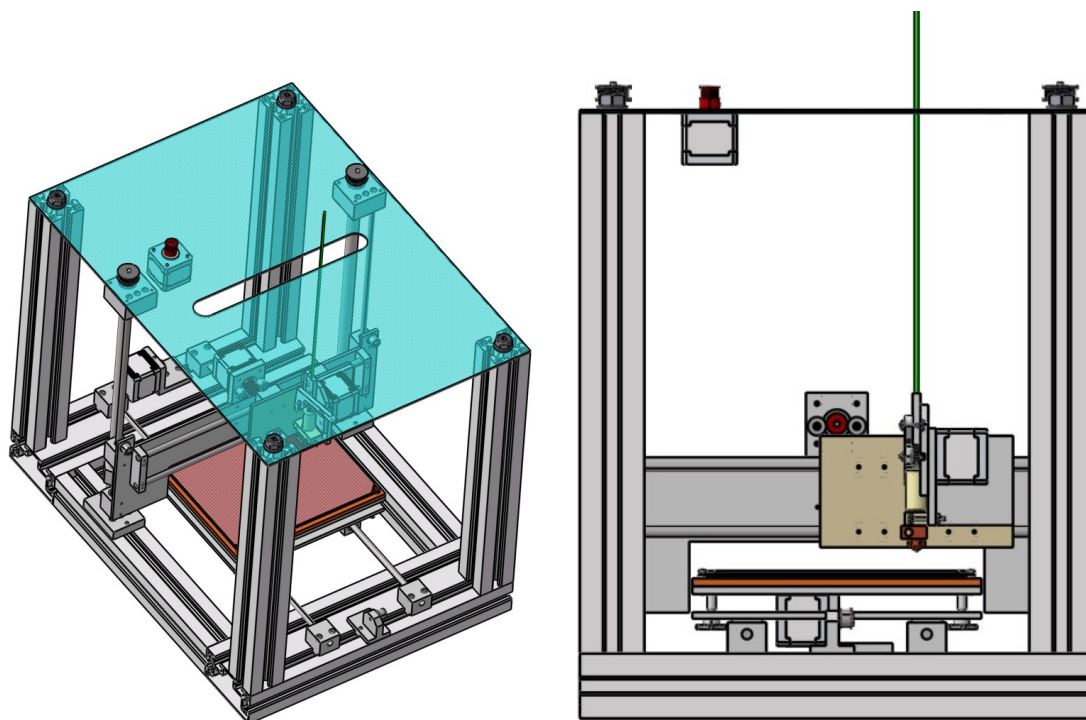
Ukázka konstrukčního návrhu - VARIANTA III
